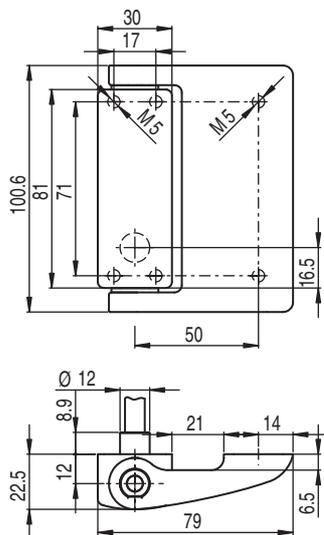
Dimensions des S410-M4-CB02M12-W et S410-M4-CB2PUR-W en mm
